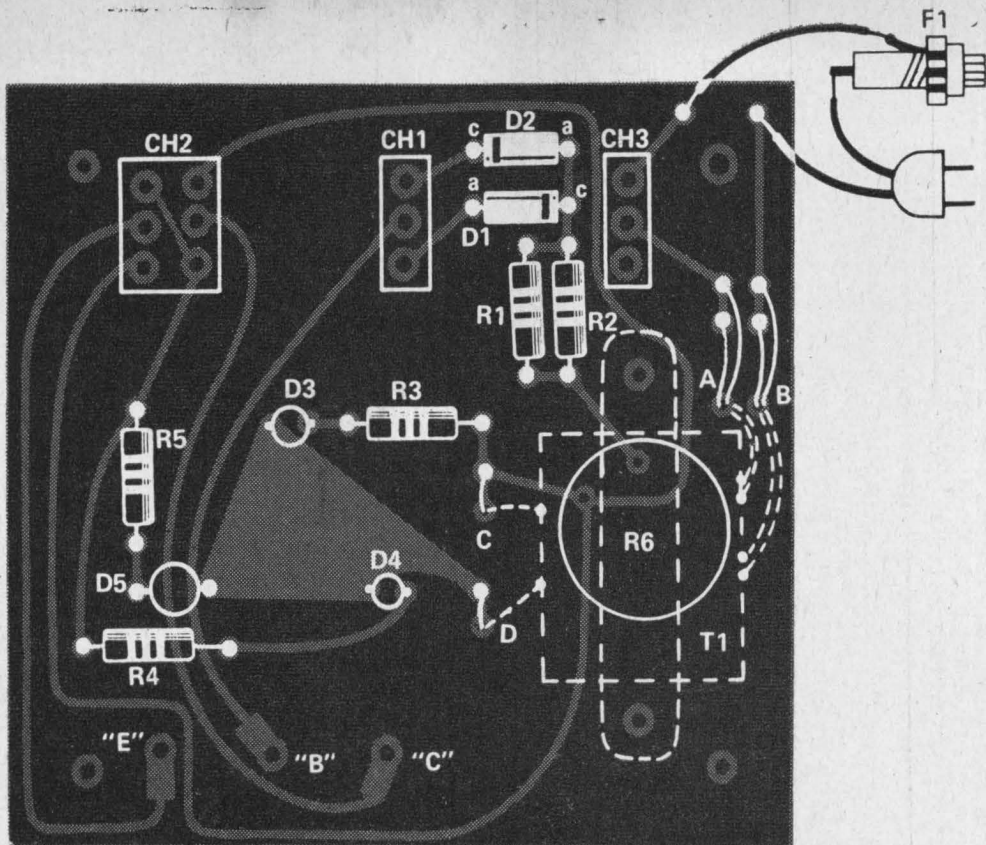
Disposição dos componentes sobre a plaqueta de circuito impresso da Fig. 2.
